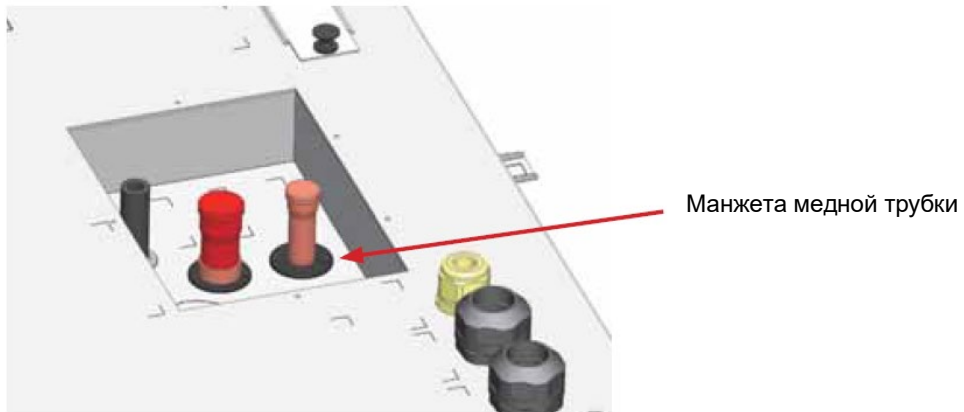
Диаметры и расположение отверстий для верхнего и нижнего трубопроводов
